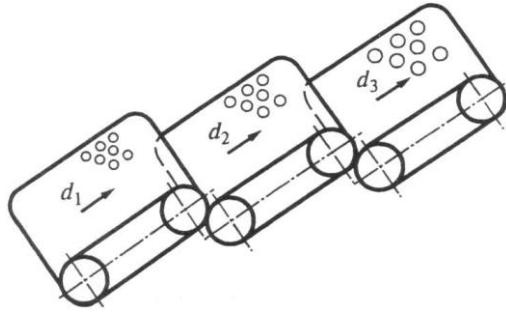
Стрічковий калібрувальний пристрій
